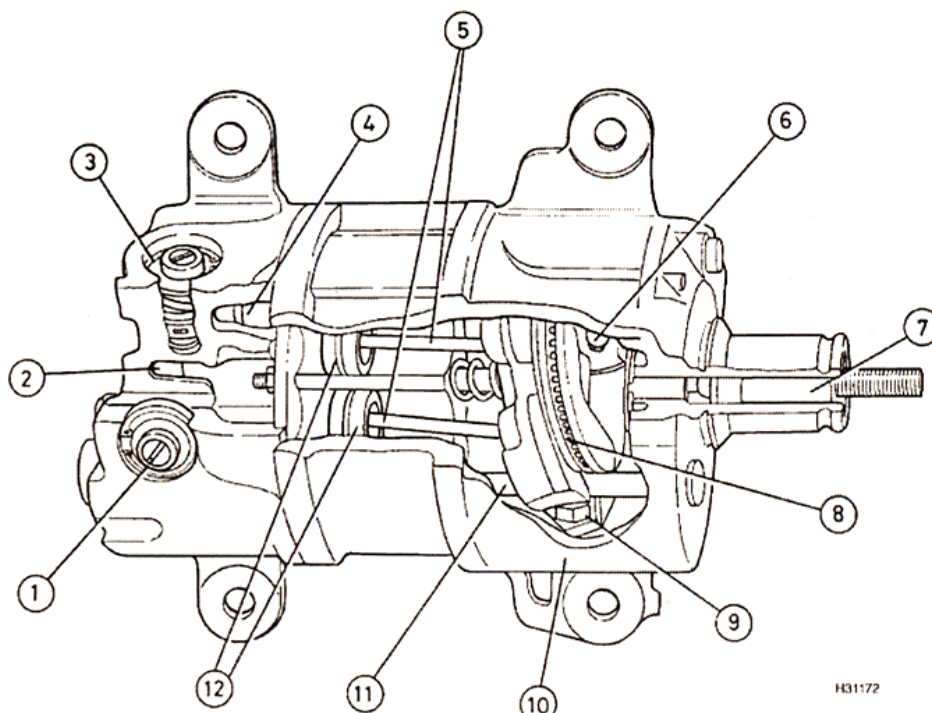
Вигляд внутрішніх порожнин класичного автомобільного компресора зі змінною продуктивністю: 1 – головний управляючий клапан; 2 – випускний отвір; 3 – допоміжний управляючий клапан; 4 – впускний отвір; 5 – шатуни; 6 – хитна шайба; 7 – вал для передачі обертання; 8 – упорний підшипник хитної шайби; 9 – стопорна шпонка; 10 – картер; 11 – вал, що попереджає обертання; 12 – поршні.
